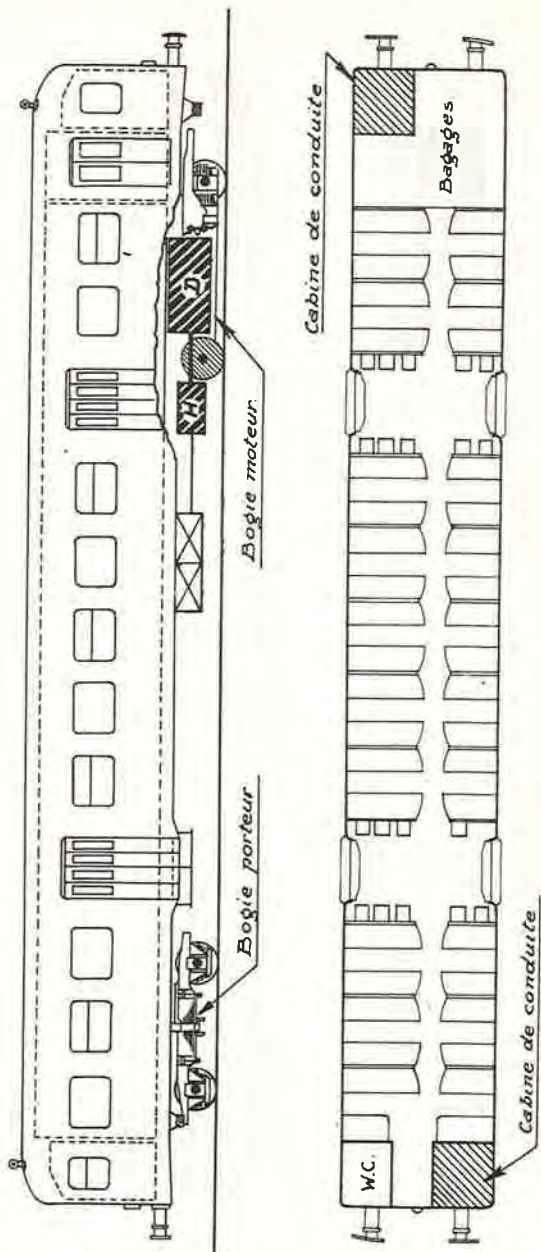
Autorail type 603 - (SEM - 400 ch.)
